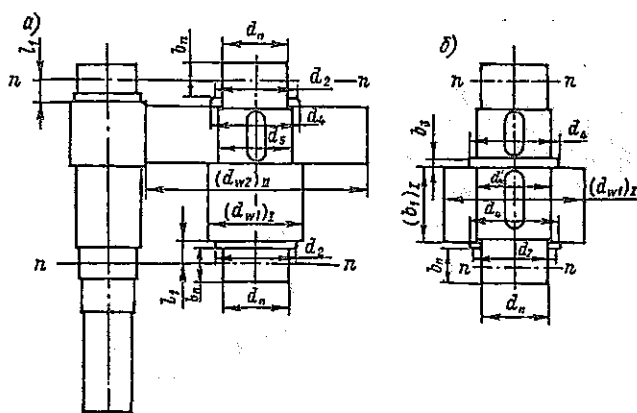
Компоновка промежуточного вала цилиндрического редуктора
